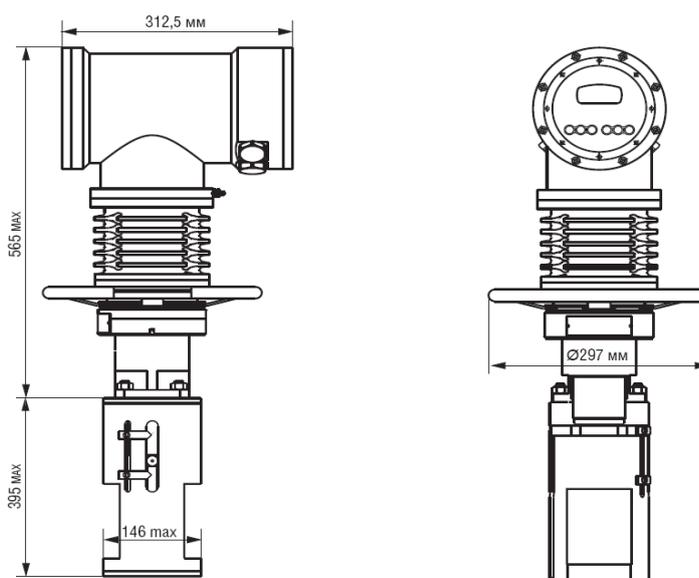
Внешний вид привода V-01-L-4,5-18000
